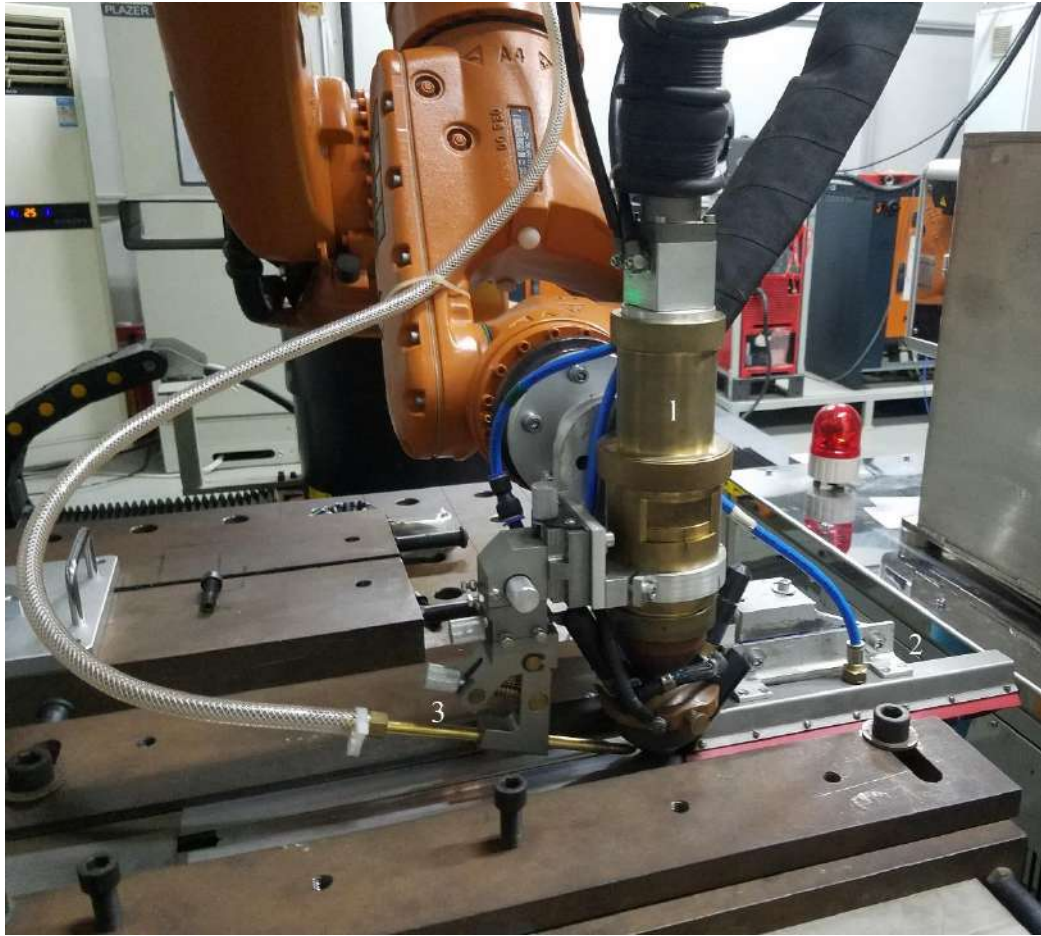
Зовнішній вигляд головки для лазерно-плазмового зварювання з антропоморфним роботом.
